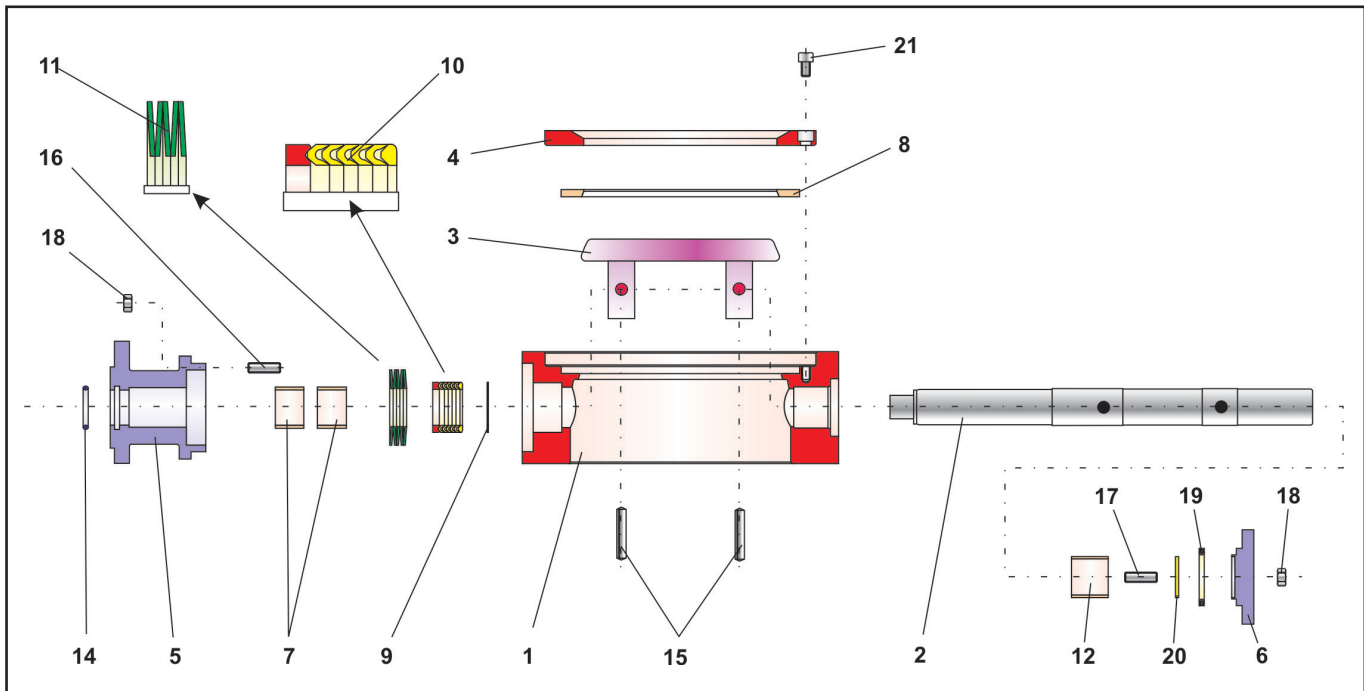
Explosionszeichnung der Stellklappe BR 14a
